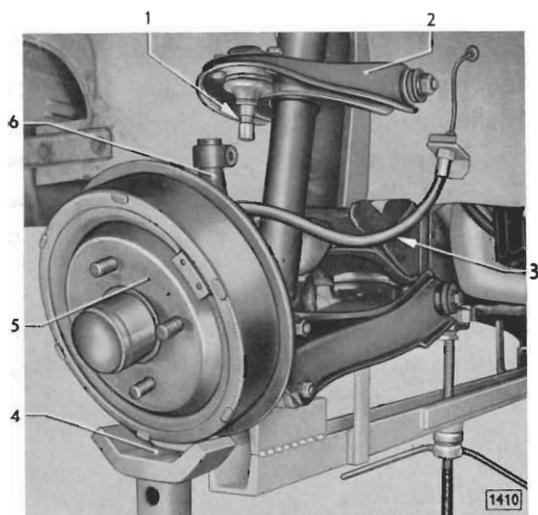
Kugelbolzenschaft aus Achsschenkelrohr ausgeführt, Bremstrommel abgestützt
